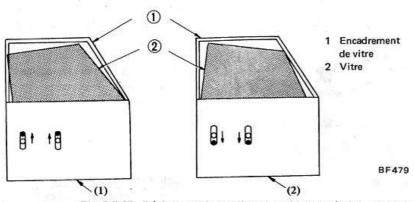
Réglage par la coulisse de guidage latéral de panneau
